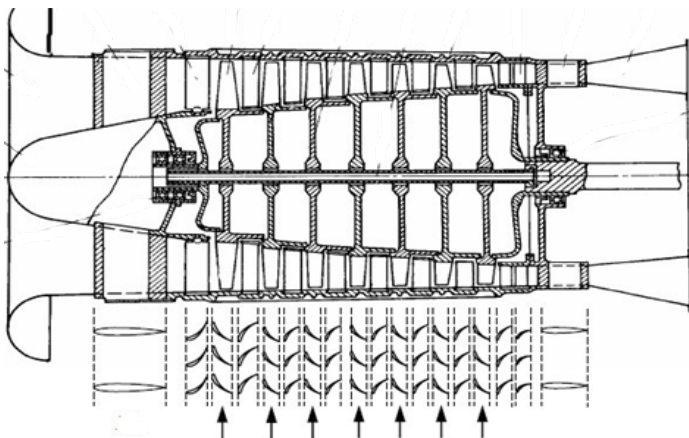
Загальний вид осьового компресора з ротором змішаного типу.
